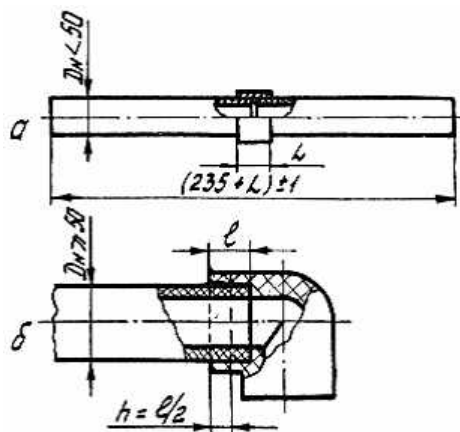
Образцы для испытаний сварных раструбных соединений: а – на сдвиг растяжением; б– на сдвиг сжатием с вырезкой кольцевого образца; L – длина муфты; l – глубина раструба; h – высота кольцевого образца
